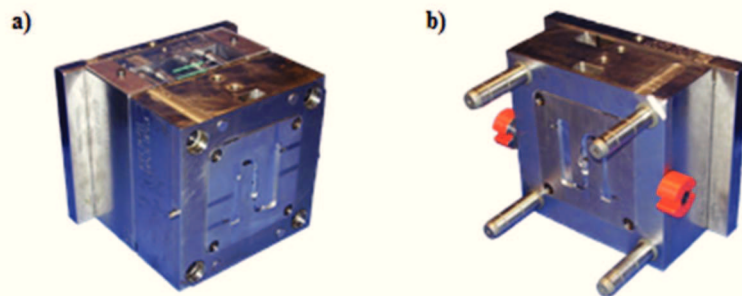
Molde de duas placas para moldação dos provetes; a) lado da extração; b) lado da injeção.
